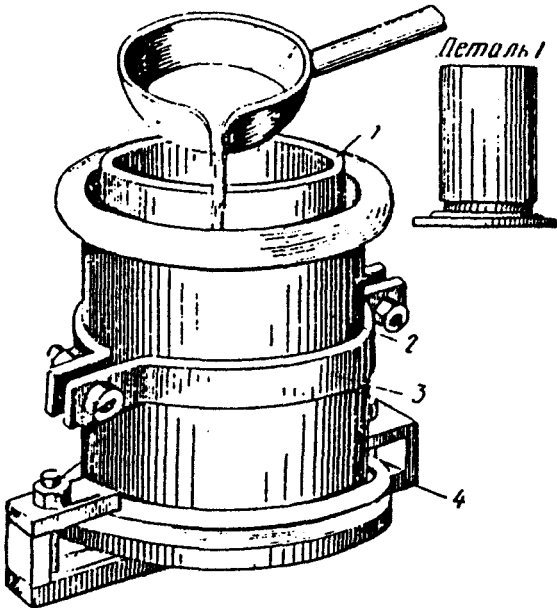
Приспособление для заливки вкладышей подшипников:
